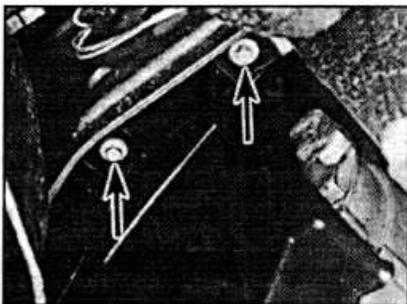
А.1. Расположение болтов крепления брызговика приводного ремня.
